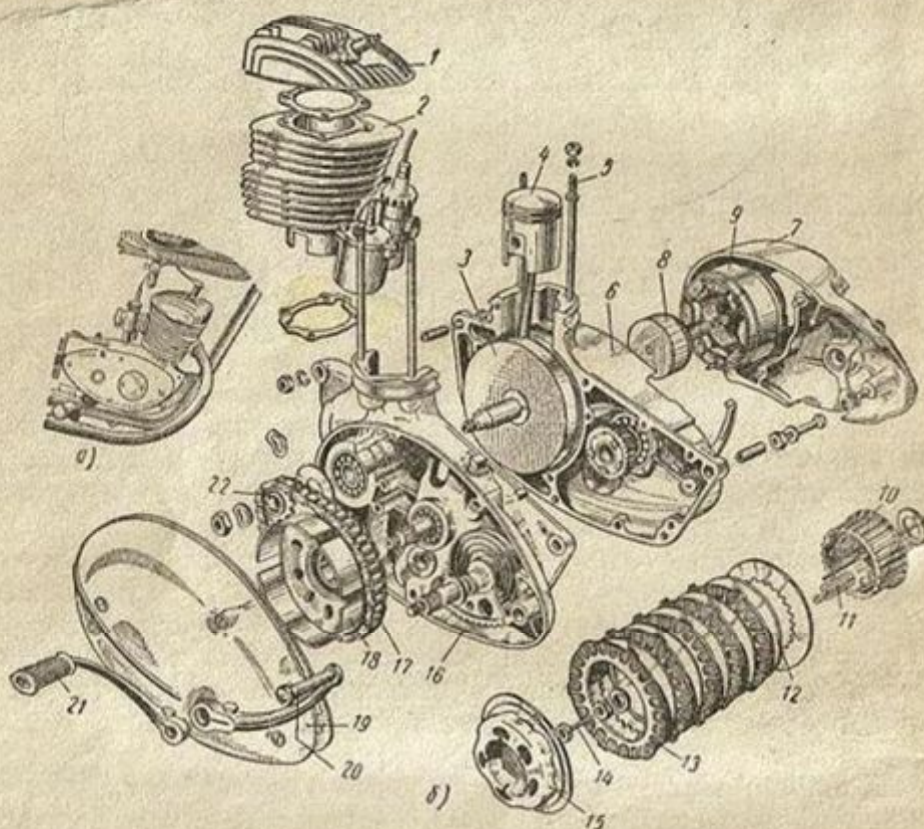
Одноцилиндровый двухтактный двигатель мотоцикла М-104:
